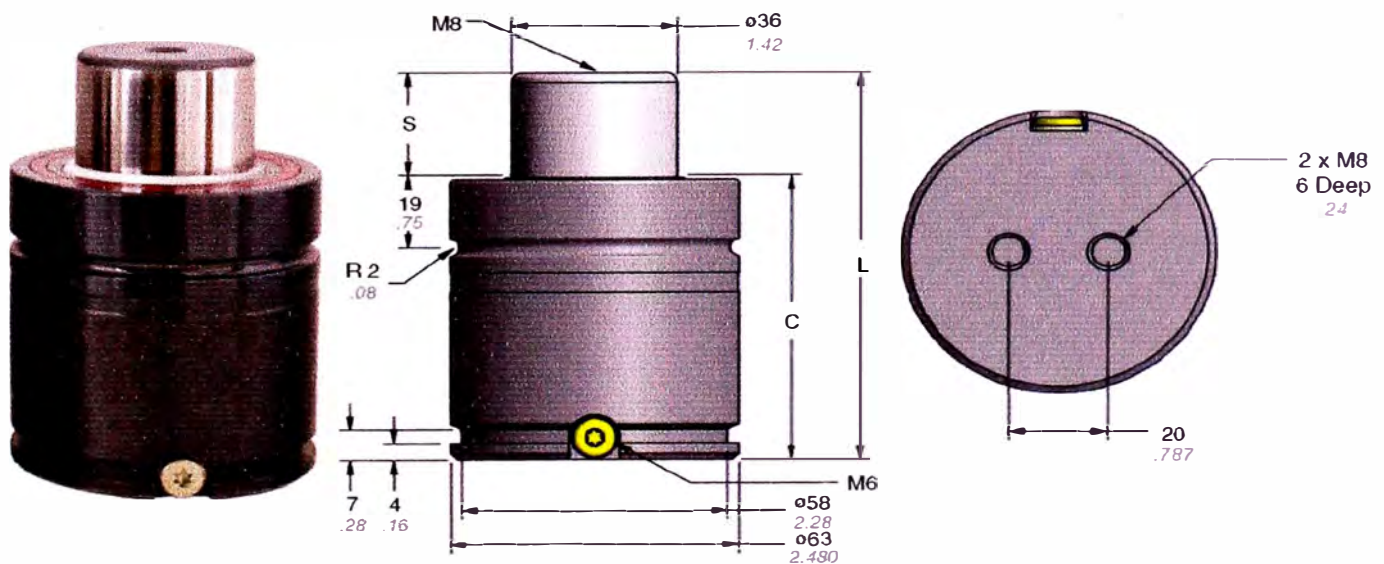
Dibujo y dimensiones del conjunto cilindro pistón.
